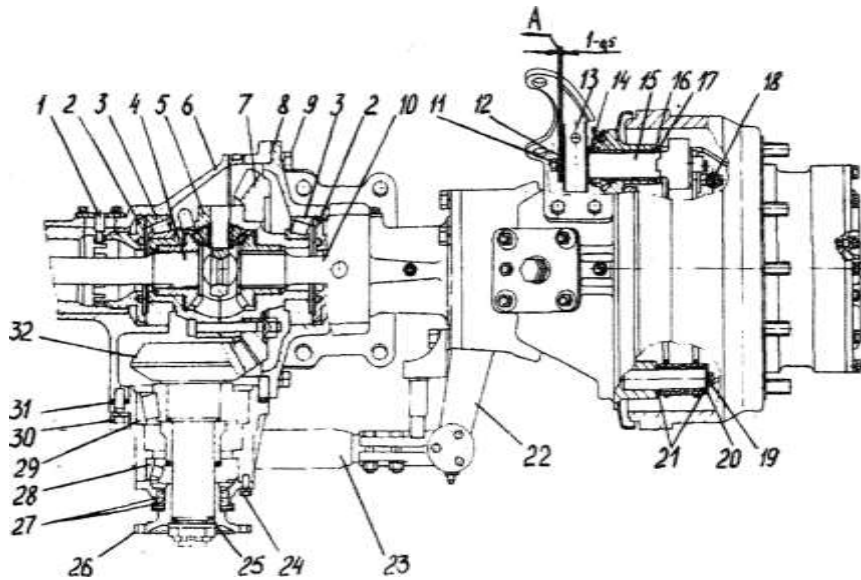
Центральний редуктор та ведучий пристрій колісних гальм:
